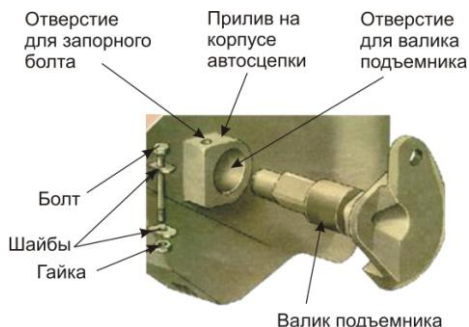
Установка валика подъемника в карман корпуса и его крепление
